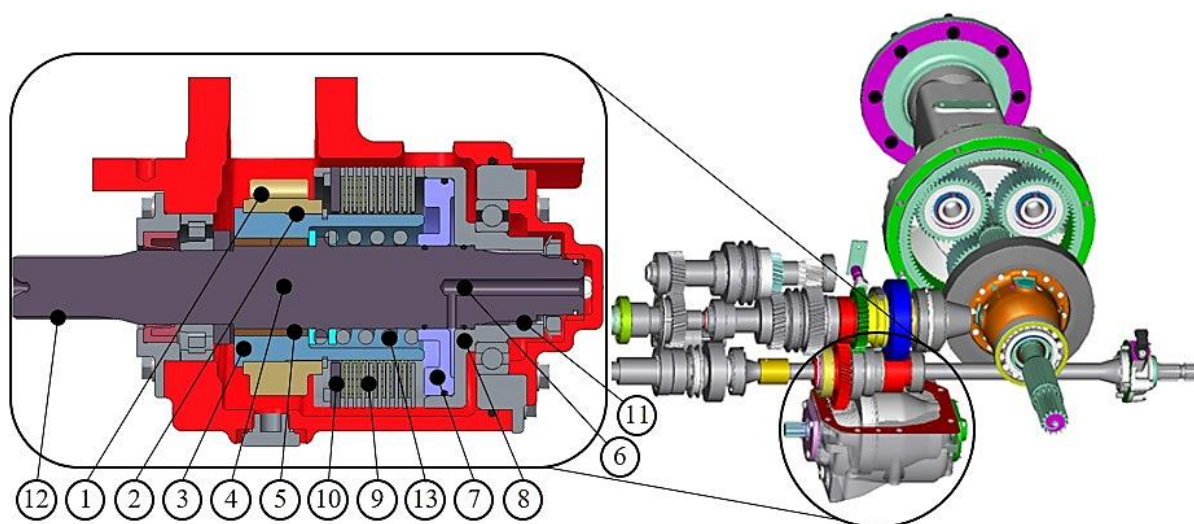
Mokrá lamelová spojka pohonu přední nápravy traktoru [4]
